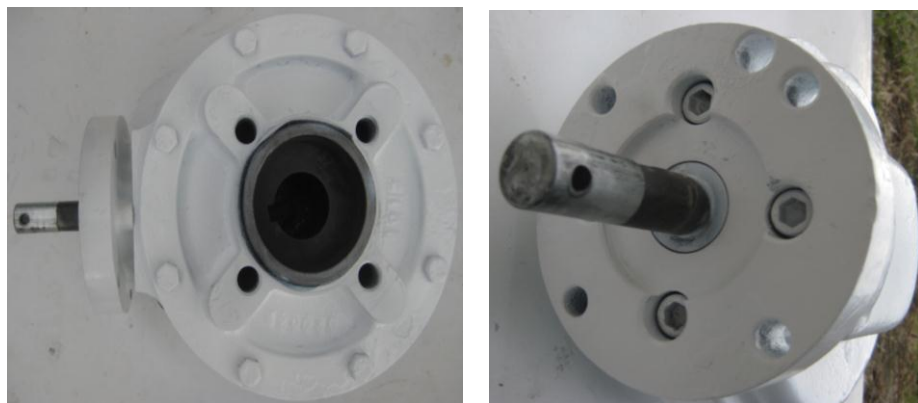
Mantenimiento y Limpieza de Caja Reductora. [3]
